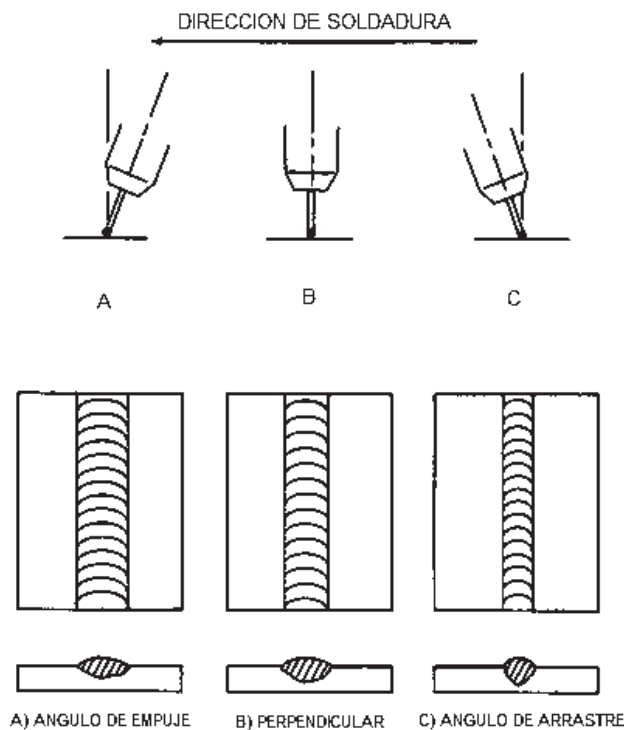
Efecto de la posición del electrodo y la técnica de soldadura sobre el cordón.
